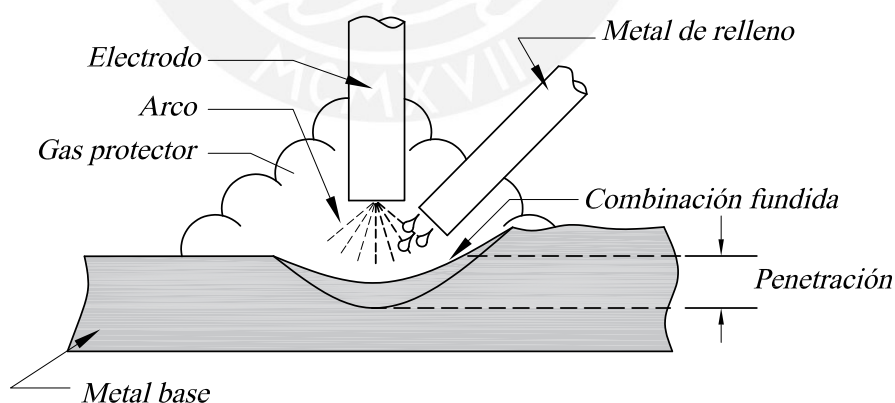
Partes de la soldadura autógena (Groover, 2012).
